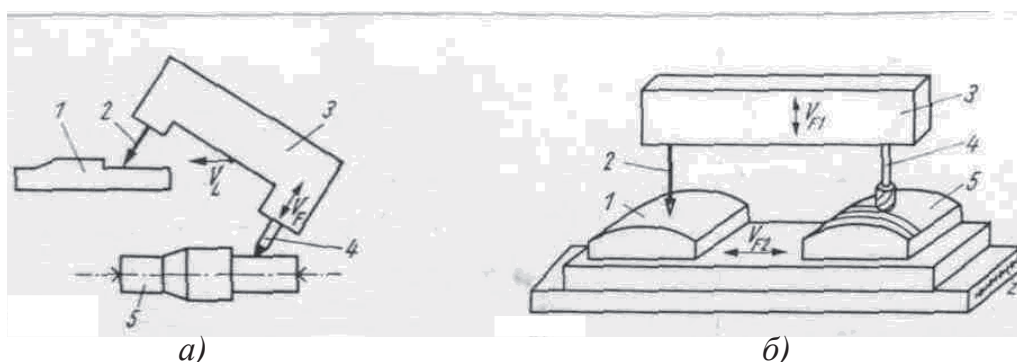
Схема обработки на копируемых станках: а – токарных; б – фрезерных
